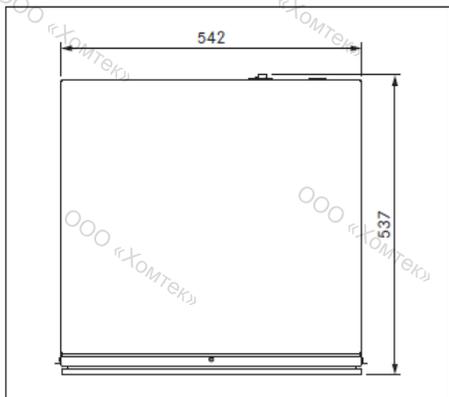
Размеры прибора, модель MS290, вид сверху
